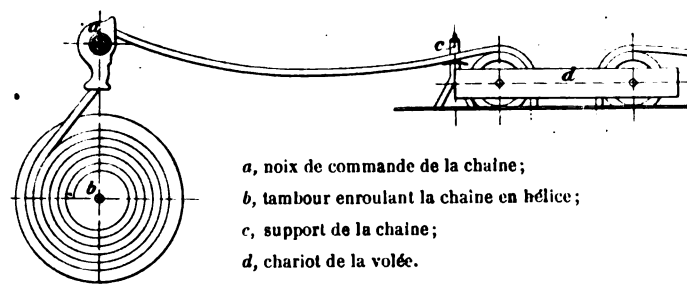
Tambour d'enroulement de la chaîne Galle.
